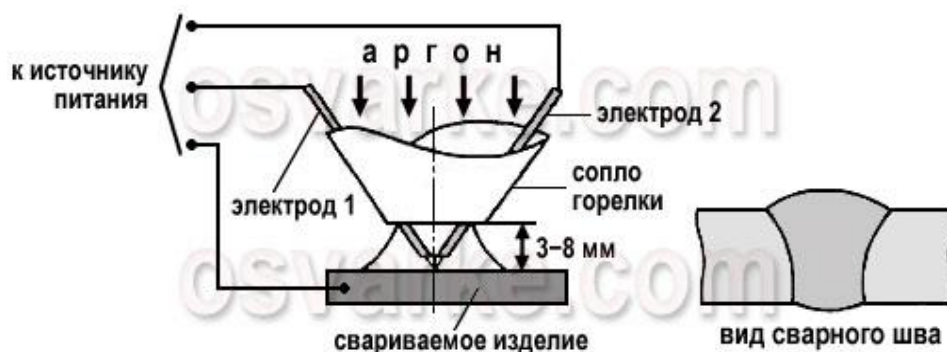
Схема сварки трёхфазной дугой
